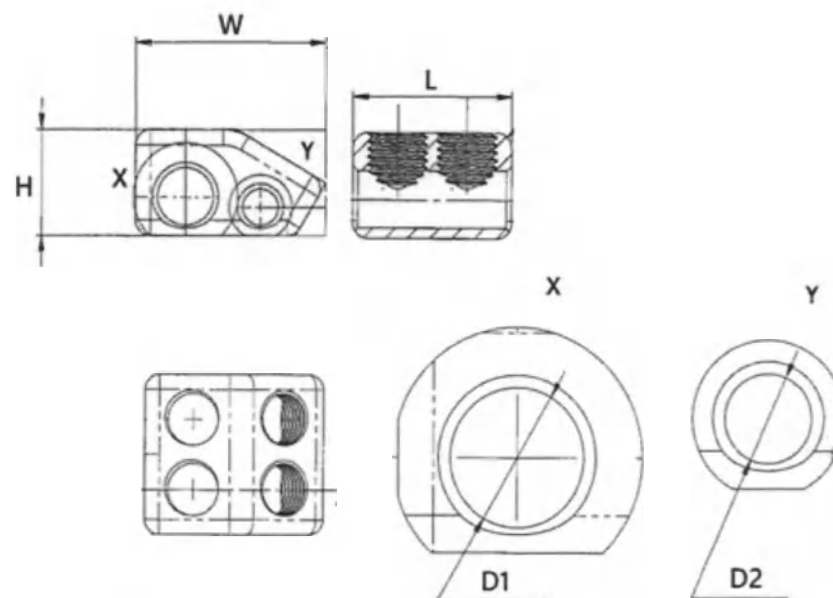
Муфта соединительная стандартная MUST MINI (4 шт./уп.)
